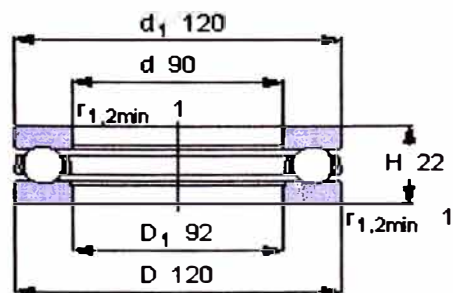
Dibujo y dimensiones del rodamiento axial.
